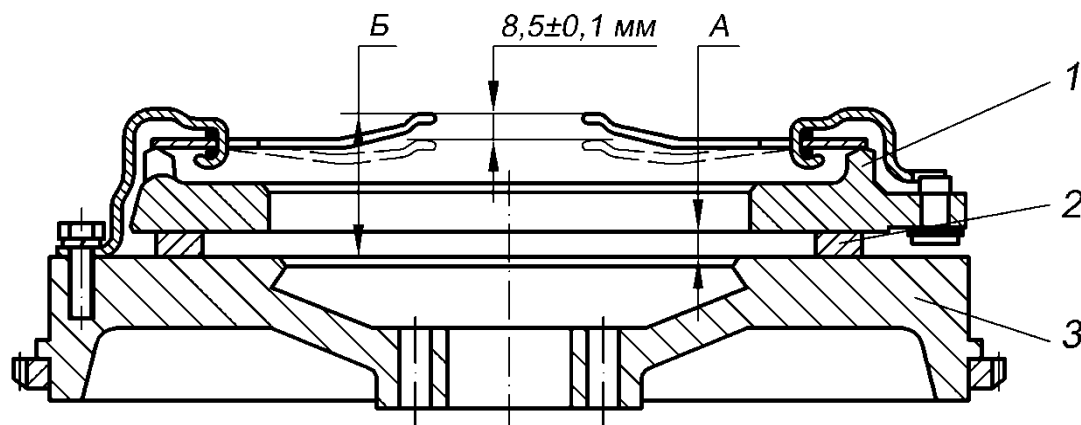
Регулировка концов лепестков и проверка нажимного диска сцепления:
